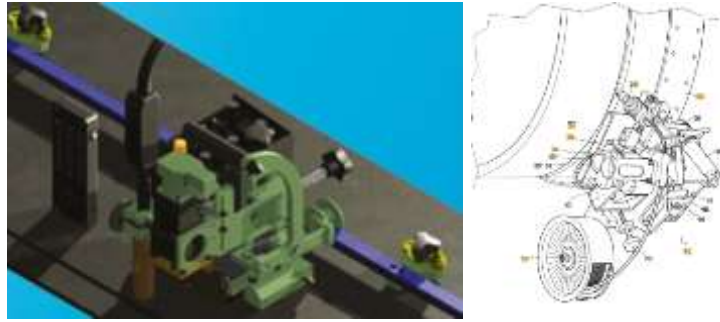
Elektro Gaz Kaynağı Kaynak Robotu ve Rayı
